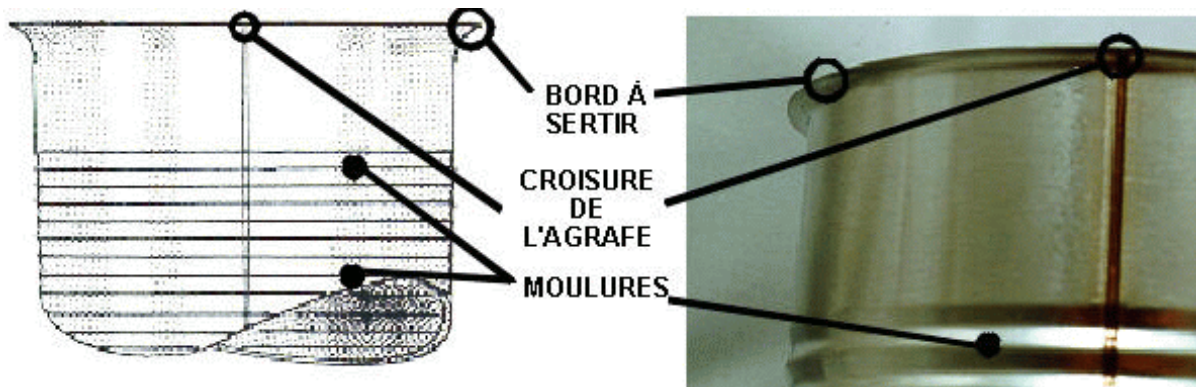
Boîte trois pièces - Agrafe électro-soudée - Boîte ouverte
